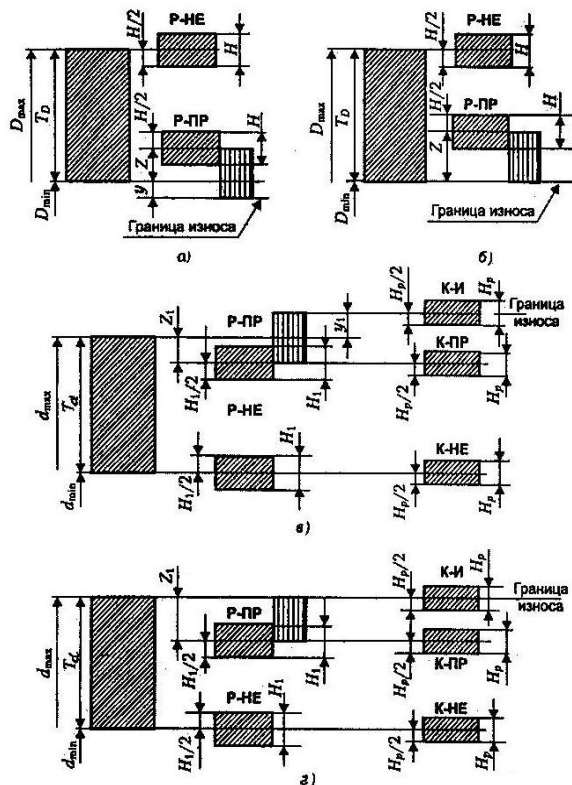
Схемы расположения допусков калибров
